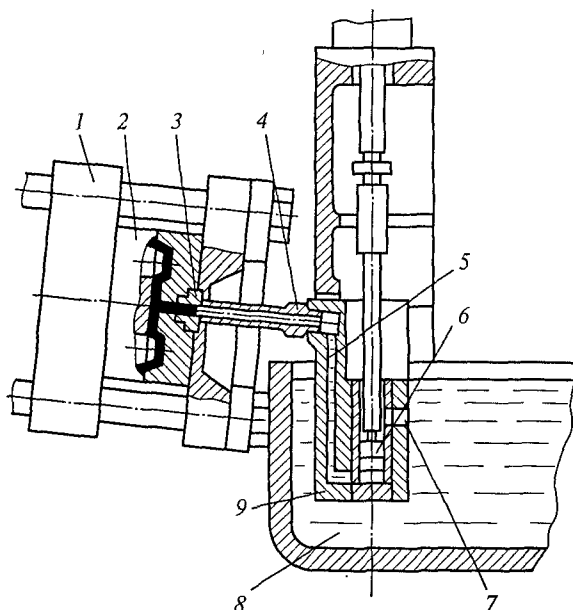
Узел прессования машины с горячей камерой прессования: 1 — подвижная плита машины; 2 — пресс-форма; 3 — литниковая втулка; 4 — мундштук; 5 — обогреваемый канал; 6 — пресс-поршень; 7 — впускное отверстие; 8 — тигель с расплавом; 9 — камера прессования
